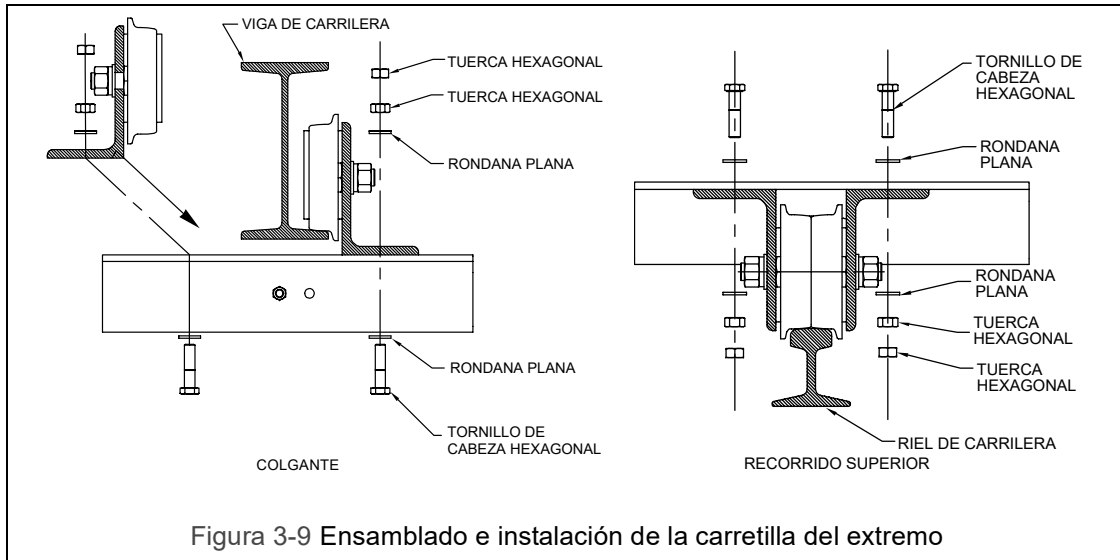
Ensamblado e instalación de la carretilla del extremo
